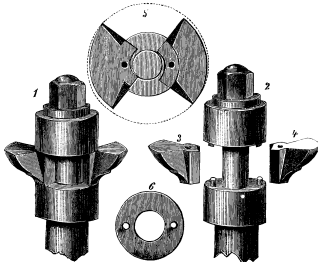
Handbetriebene Holzbearbeitungsmaschine.
